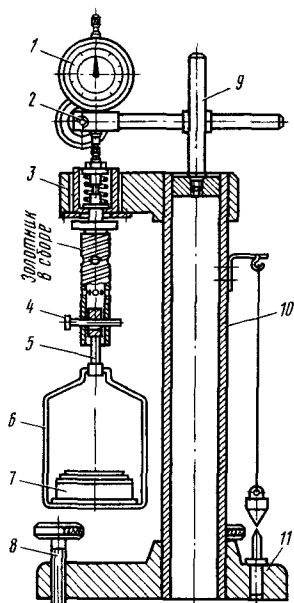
Приспособление для регулировки затяжки компенсирующей пружины:
